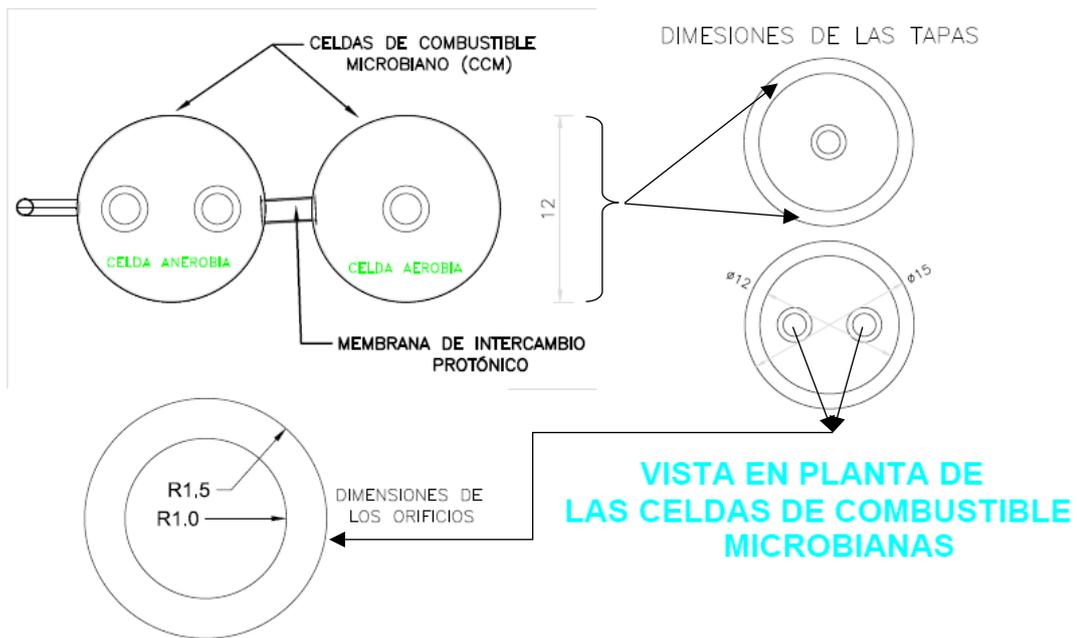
Vista en planta 2D de las CCM, dimensiones de las tapas y orificios.
